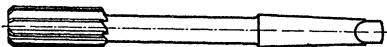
Maschinenreibahle mit kegelförmigem Schaft.
